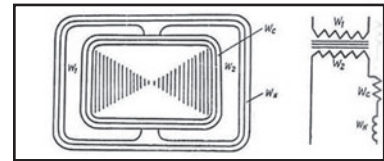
Схема трансформатора ТСМ-250, регульованого зварювальним кабелем за а.с. № 218356
